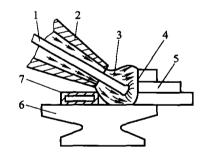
直流电机电枢绕组氩弧焊示意图 1-电极; 2-喷嘴; 3-氩气层流; 4-电弧; 5 绕组引出线头; 6 换向片; 7-水冷环套
